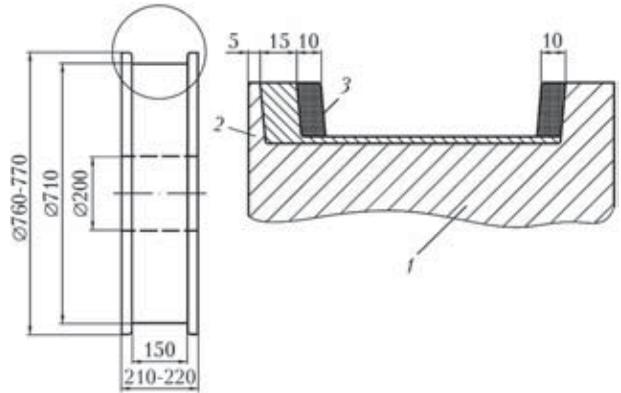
Схема наплавки крановых колес: 1 — основной металл; 2, 3 — наплавленный металл, полученный с использованием проволоки соответственно ВЕЛТЕК-Н300РМ и ВЕЛТЕК-Н280РМ
